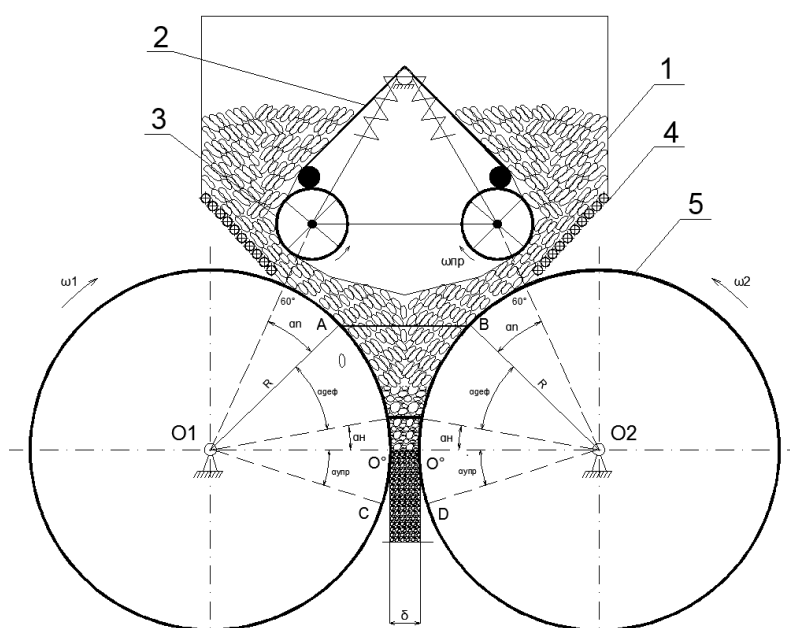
Схема пресс-валкового измельчителя с зубчатыми валками для измельчения сланцевых материалов: 1 – устройство для направленной подачи материала; 2 – подвижные щеки; 3, 4 – направляющие валики; 5 – зубчатые валки
